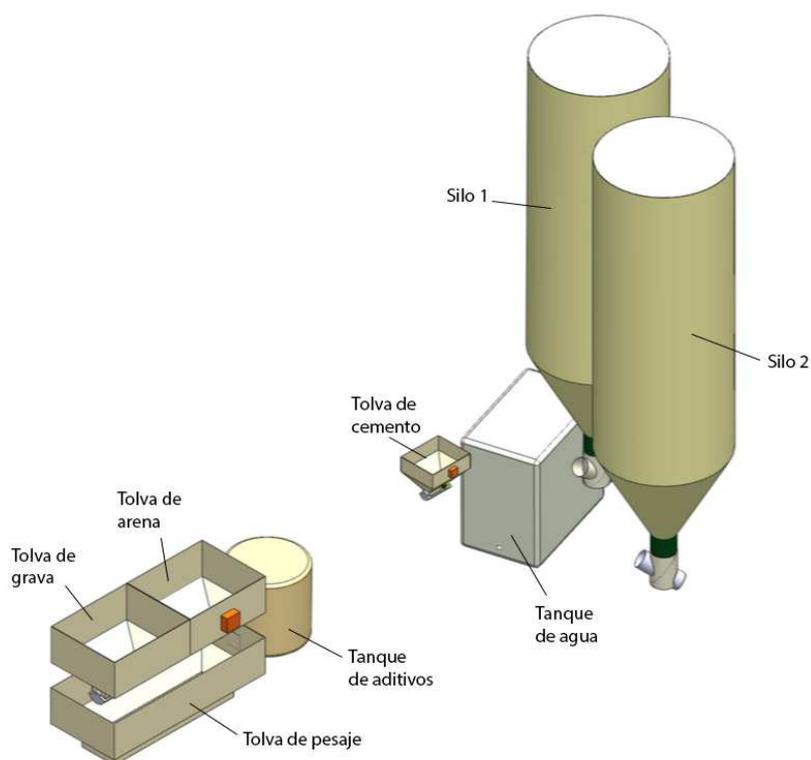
Sistema de almacenamiento de la planta dosificadora de hormigón
